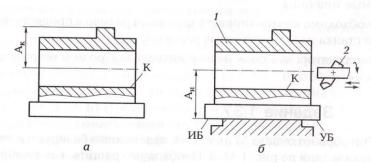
Схема растачивания отверстия при неподвижной детали: a — чертеж конструктора;  $\delta$  — выбор исходной базы (ИБ = УБ)
